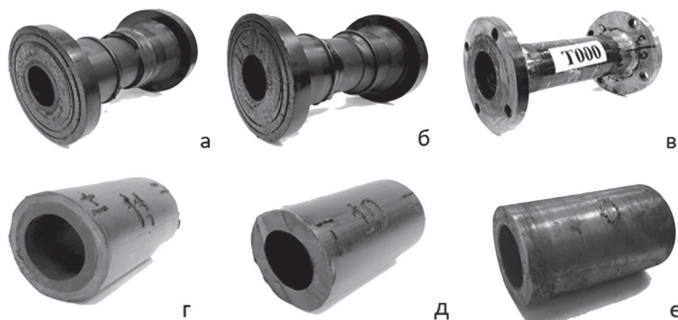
Образцы для испытаний. а – образец №1, б – образец №2, в – образец №3, г – образец №4, д – образец №5, е – образец №6.
